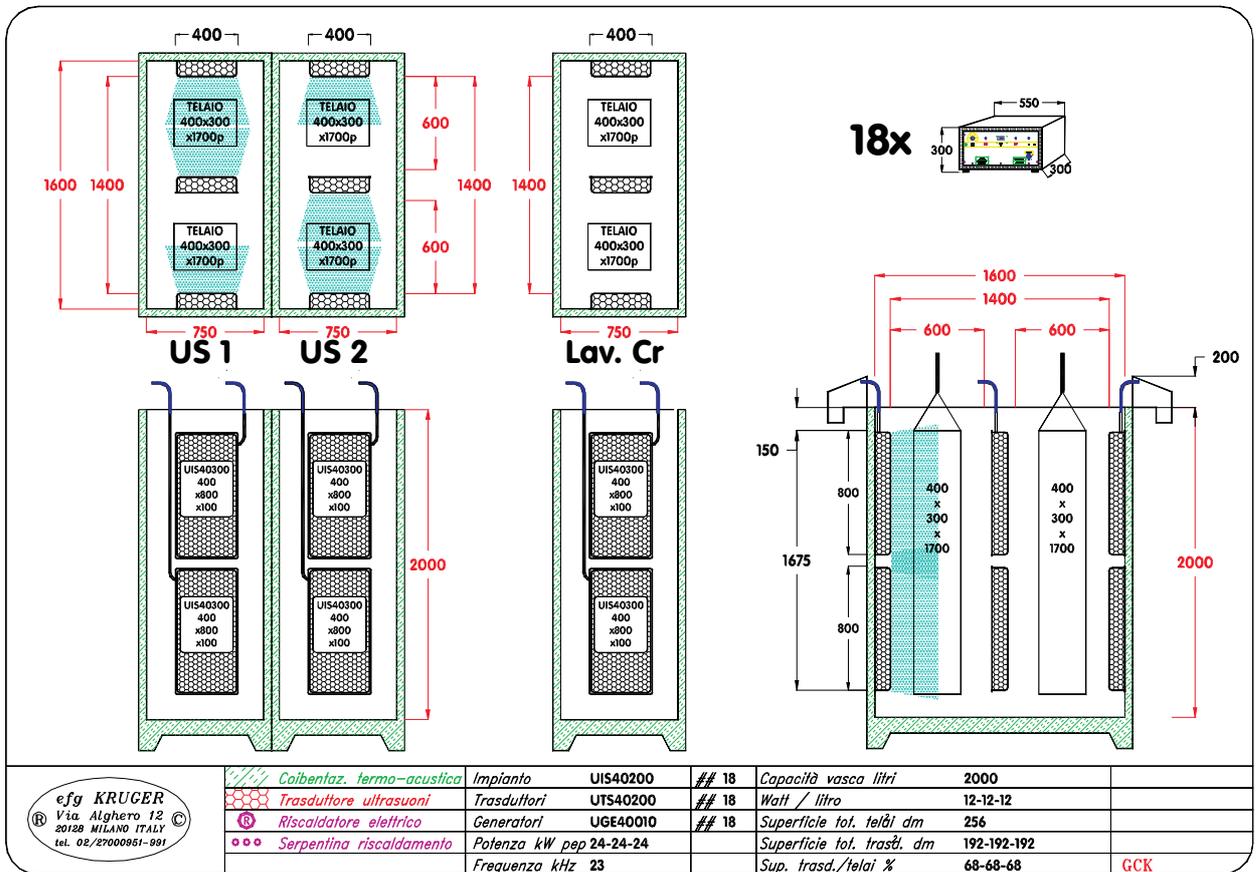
Dimensionamento impianto a ultrasuoni per impianto a braccia.
